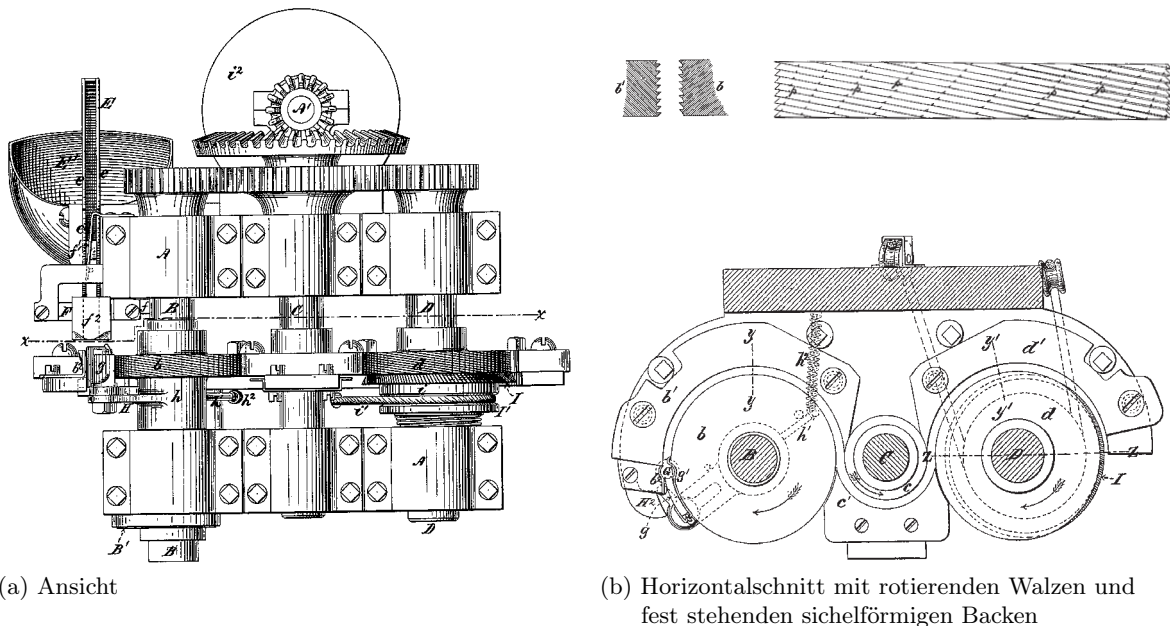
Maschine zum Aufrollen des Schraubengewindes von Hayward Augustus Harvey
